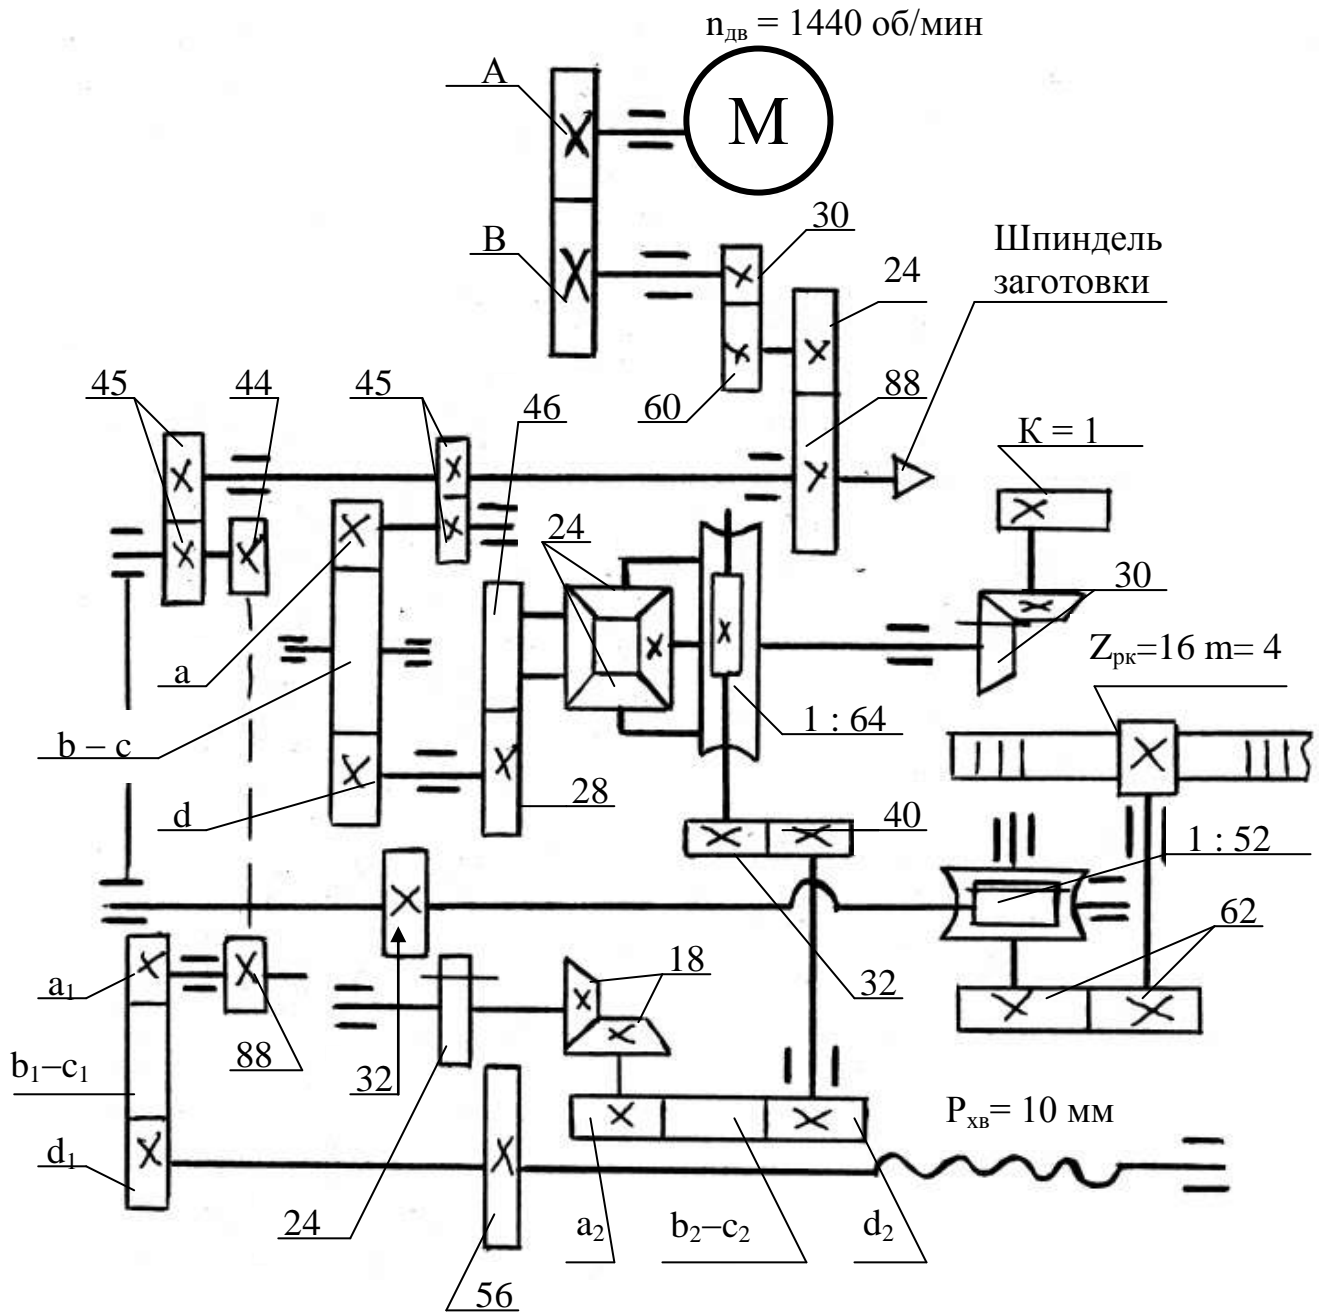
Кинематическая схема токарно-затыловочного станка:
